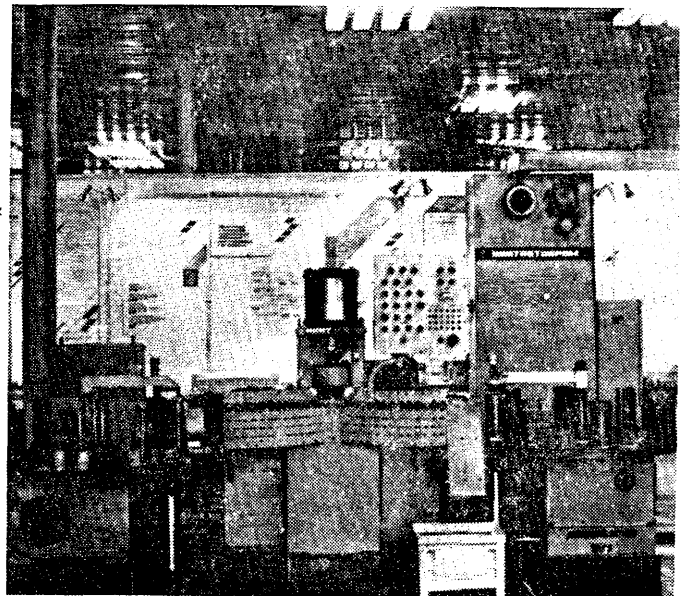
Автомат мод. 5081 для сборки держателя манжеты
